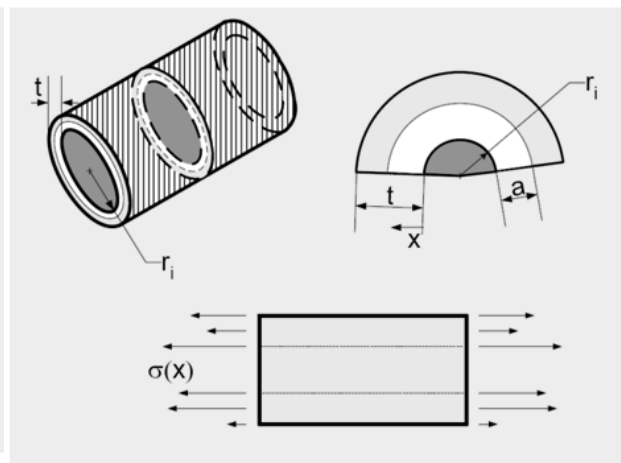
Hohlzylinder, langer Oberflächenriss innen [58]
